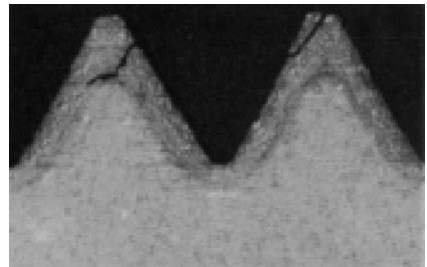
Zu tief nitriertes Gewinde mit abgeplatzenen Gewindespitzen.
